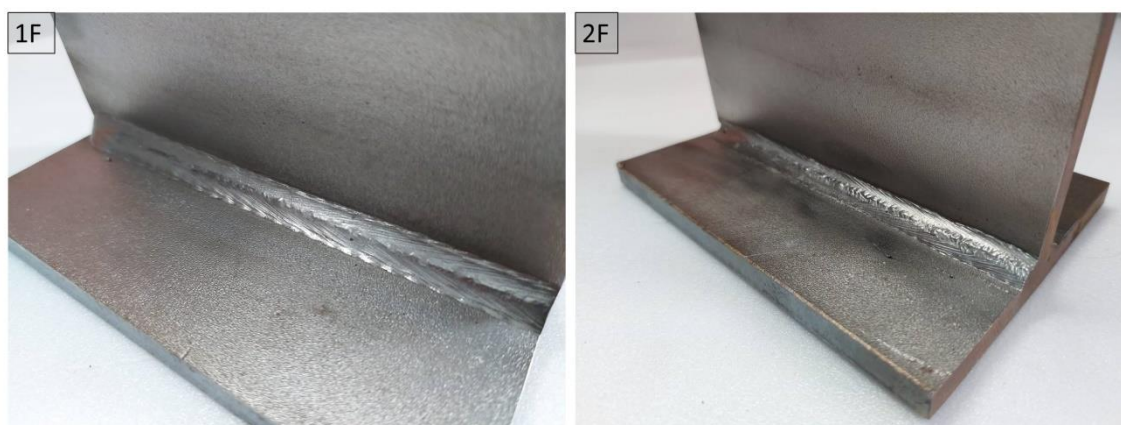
Aspecto visual obtido em testes in loco para cordão a5 e posições 1F e 2F soldados após redefinição dos parâmetros de solda conforme Tabela 11.
